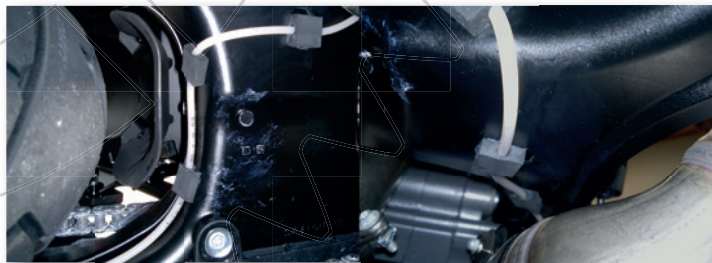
Verlegung der Ölleitung von der Innenseite der Schwinge über die Schwingenbrücke auf die nicht kettenführende Unterseite der Schwinge
